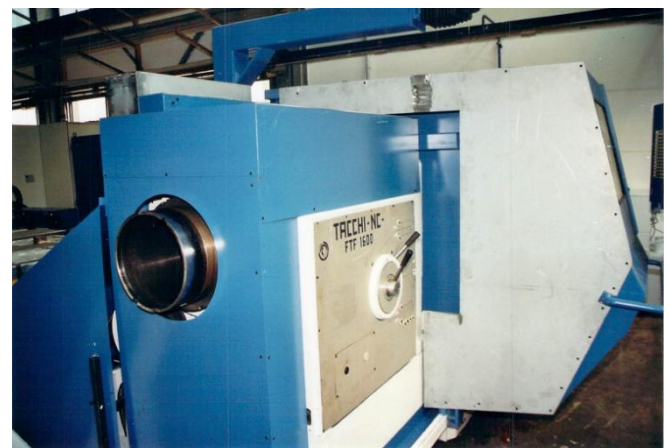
Die Maschine hat auch eine grosse Spindelbohrung wie eine Oelfeld Drehmaschine.
